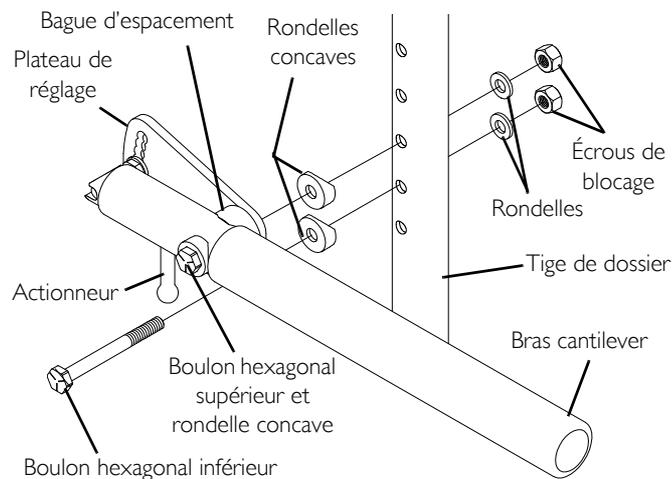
Installation des bras cantilever verrouillables. - Réglage de la hauteur du bras cantilever verrouillable.
